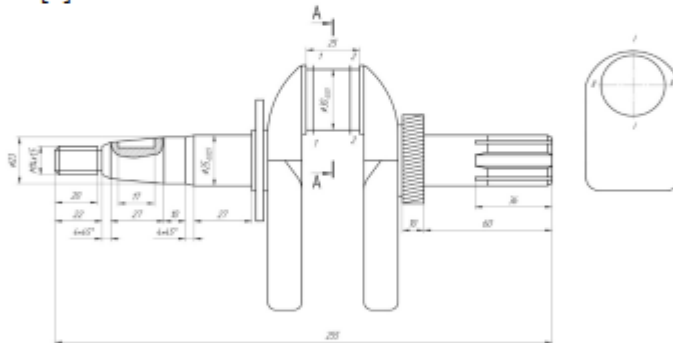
Схема вимірювання колінчатого валу в місцях розміщення шатунного підшипника
